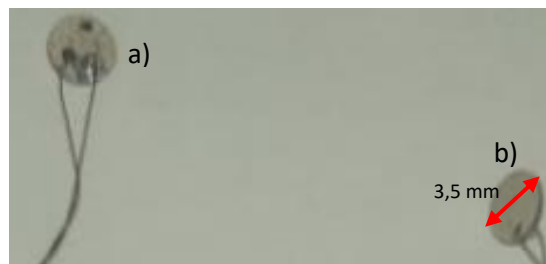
Piezoelétricos soldados: a) Soldado a olho nu b) Soldado com a montagem.
